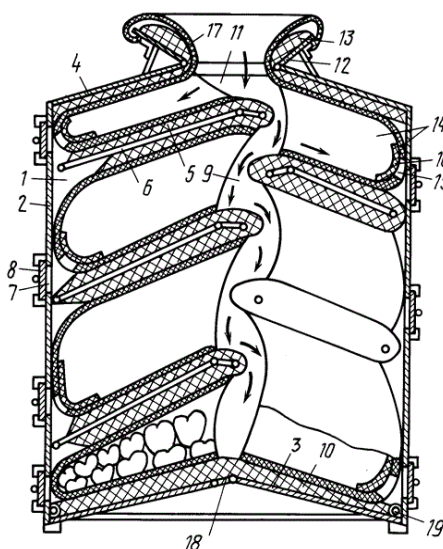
контейнер для хранения и транспортировки плодов и овощей (Патент RU 2014261): 1 – фронтальная стенка, 2 – боковая стенка, 3 – дно, 4 – крышка, 5 – полка, 6 – армированная жесткая сетка, 7 – выгрузное окно, 8 – кромка плоскости, 9 – наклоненный канал, 10 – эластичная оболочка, 11 – люк, 12 – створка, 13 – прокладка, 14 – мешок, 15 – выгрузное отверстие, 16 – клапан, 17 – рукав, 18 – гибкая связь, 19 – петля.
